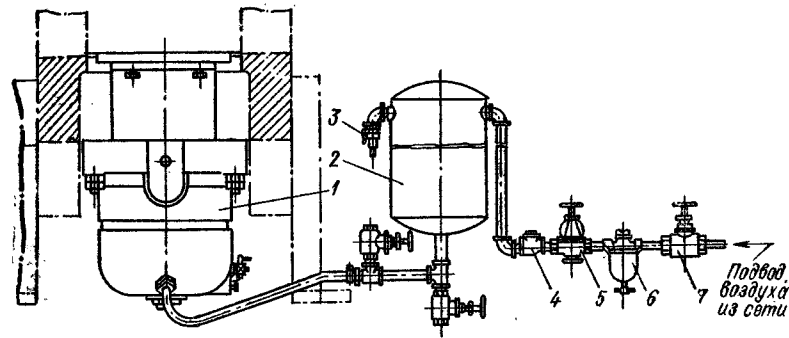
Схема присоединения пневматического буфера к сети сжатого воздуха: 1 — цилиндр буфера; 2 — ресивер; 3 — предохранительный клапан; 4 — обратный клапан; 5 — редукционный клапан; 6 — фильтр; 7 — сетевой вентиль
